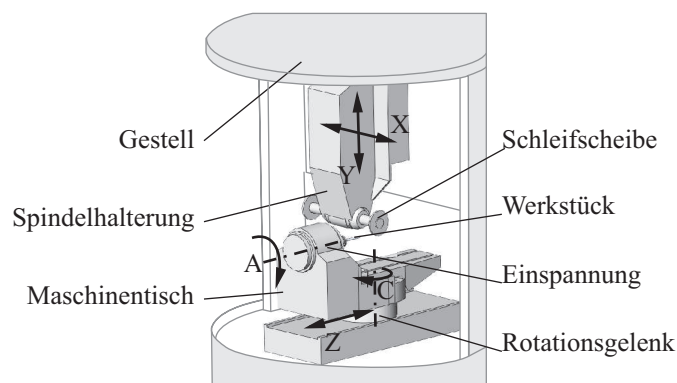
Struktur der betrachteten 5-Achsen CNC Werkzeugschleifmaschine
